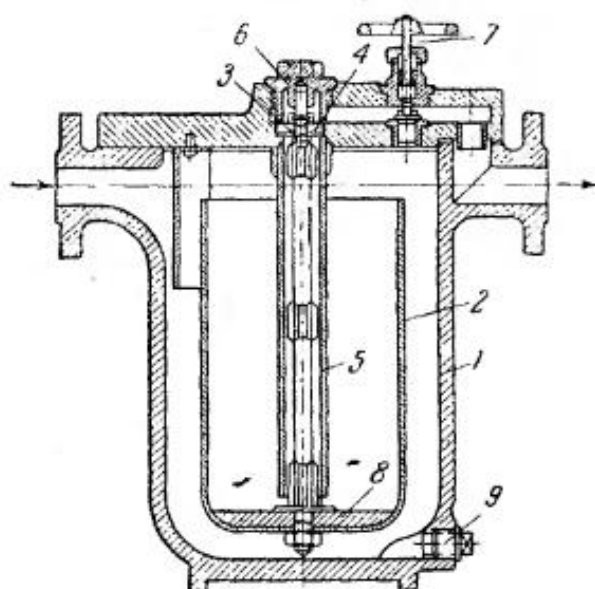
Конденсационный горшок с открытым поплавком: 1— корпус; 2— поплавок; 3—клапан; 4—сменная шайба; 5—трубка; 6— обратный клапан; 7—продувочный вентиль; 8—сменный груз; 9— пробка
